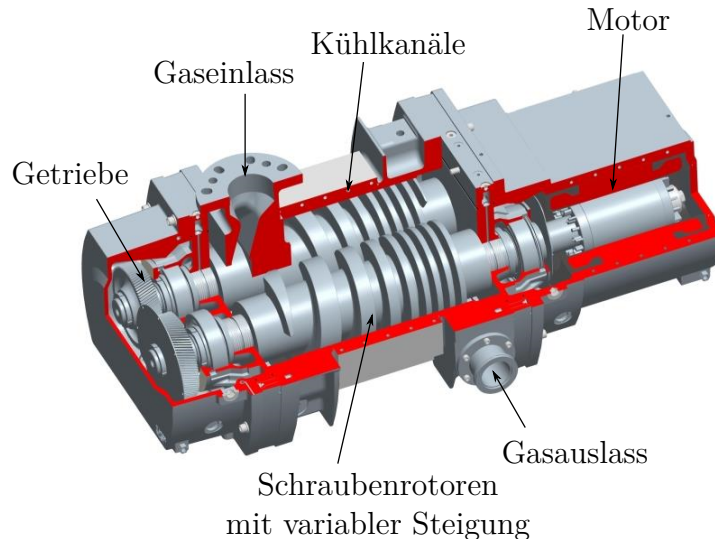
Aufbau einer modernen Schraubenvakuumpumpe.
